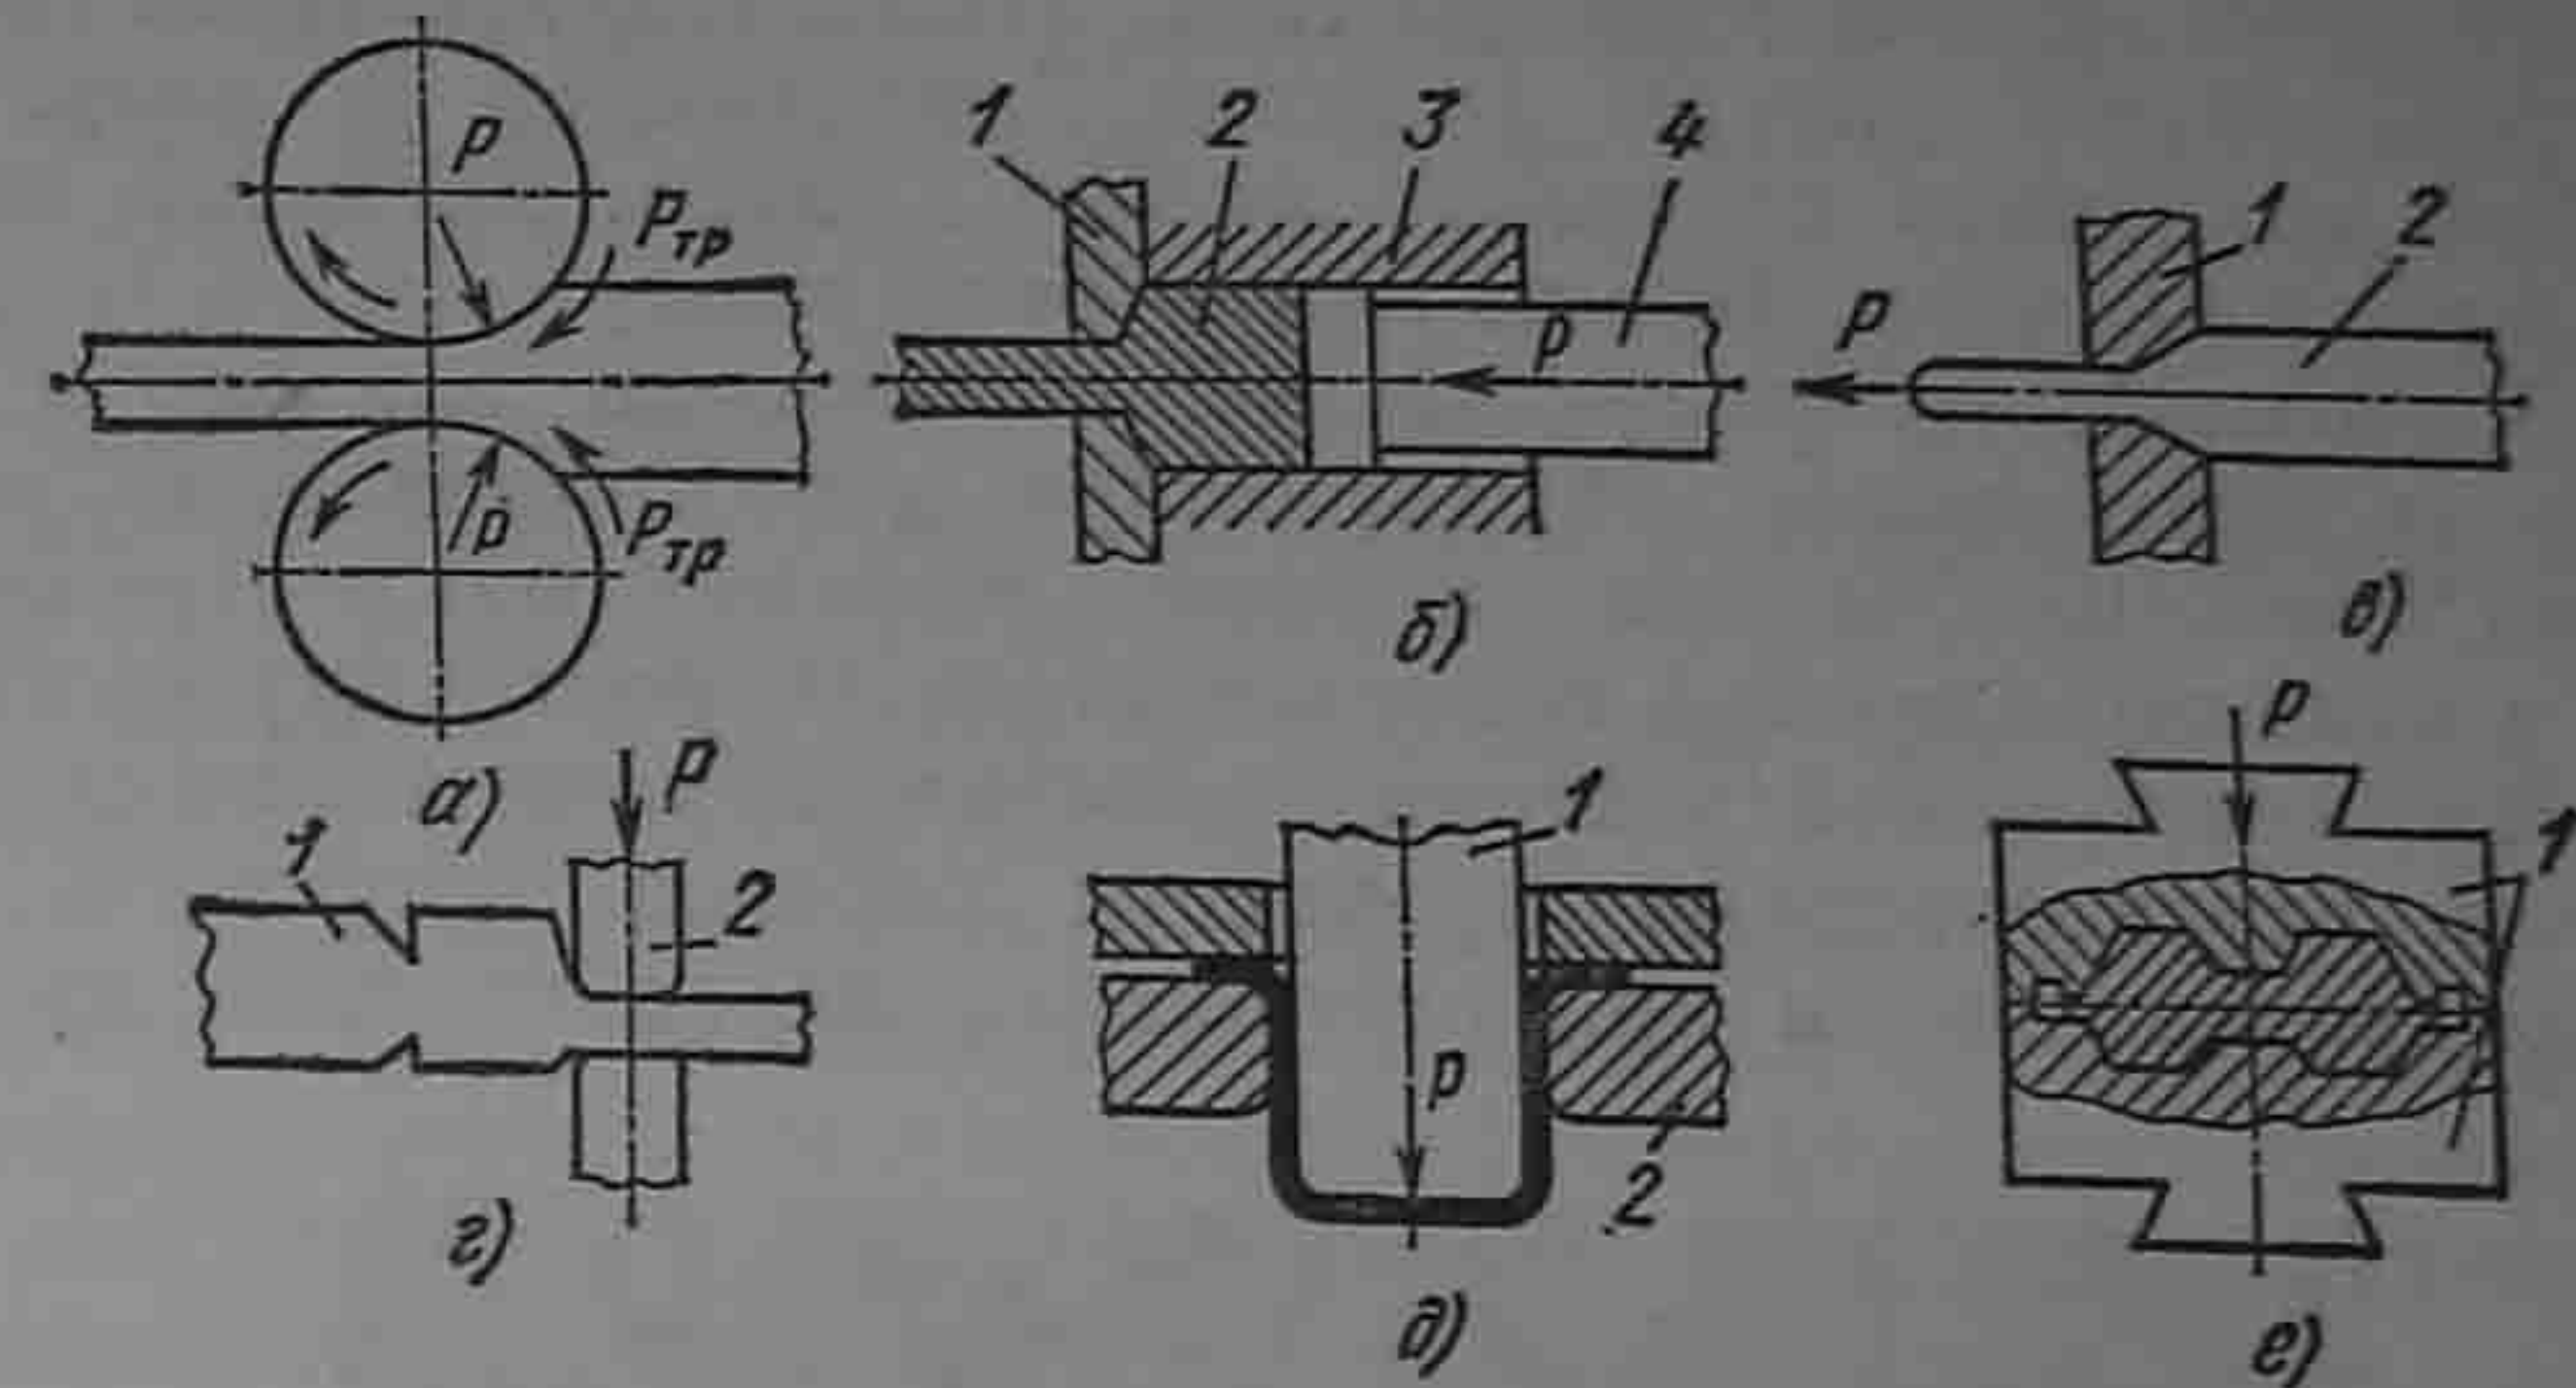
Схемы основных видов обработки металлов давлением: а — прокатки; б — прессования; в — волочения; г —ковки; д — одного из процессов листовой штамповки; е — одного из процессов объемной штамповки
